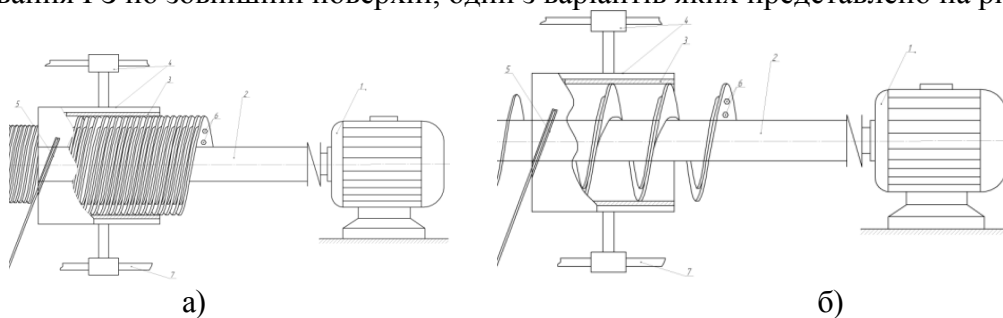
Способи формування гвинтових заготовок по зовнішній поверхні:
